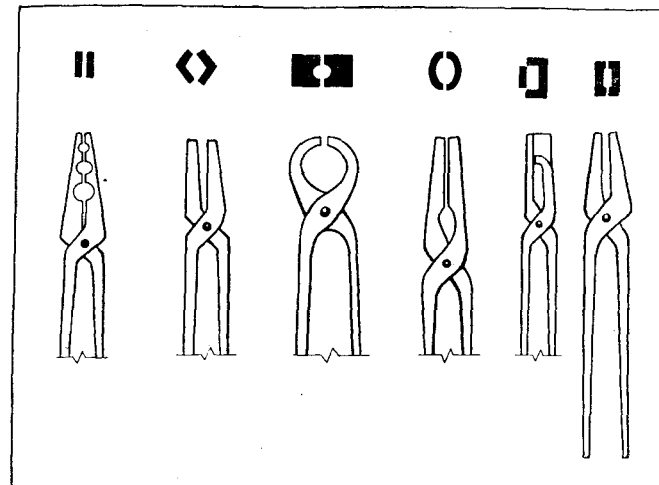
Формы губок кузнечных клещей для удерживания заготовок различной формы и сечения
